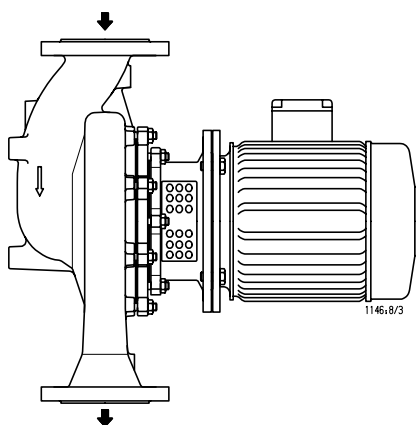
Горизонтальная установка, направление потока сверху вниз. Корпус насоса следует повернуть на 180° так, чтобы отверстия для отвода конденсата были направлены вниз, и клеммная коробка осталась в настоящем положении.
